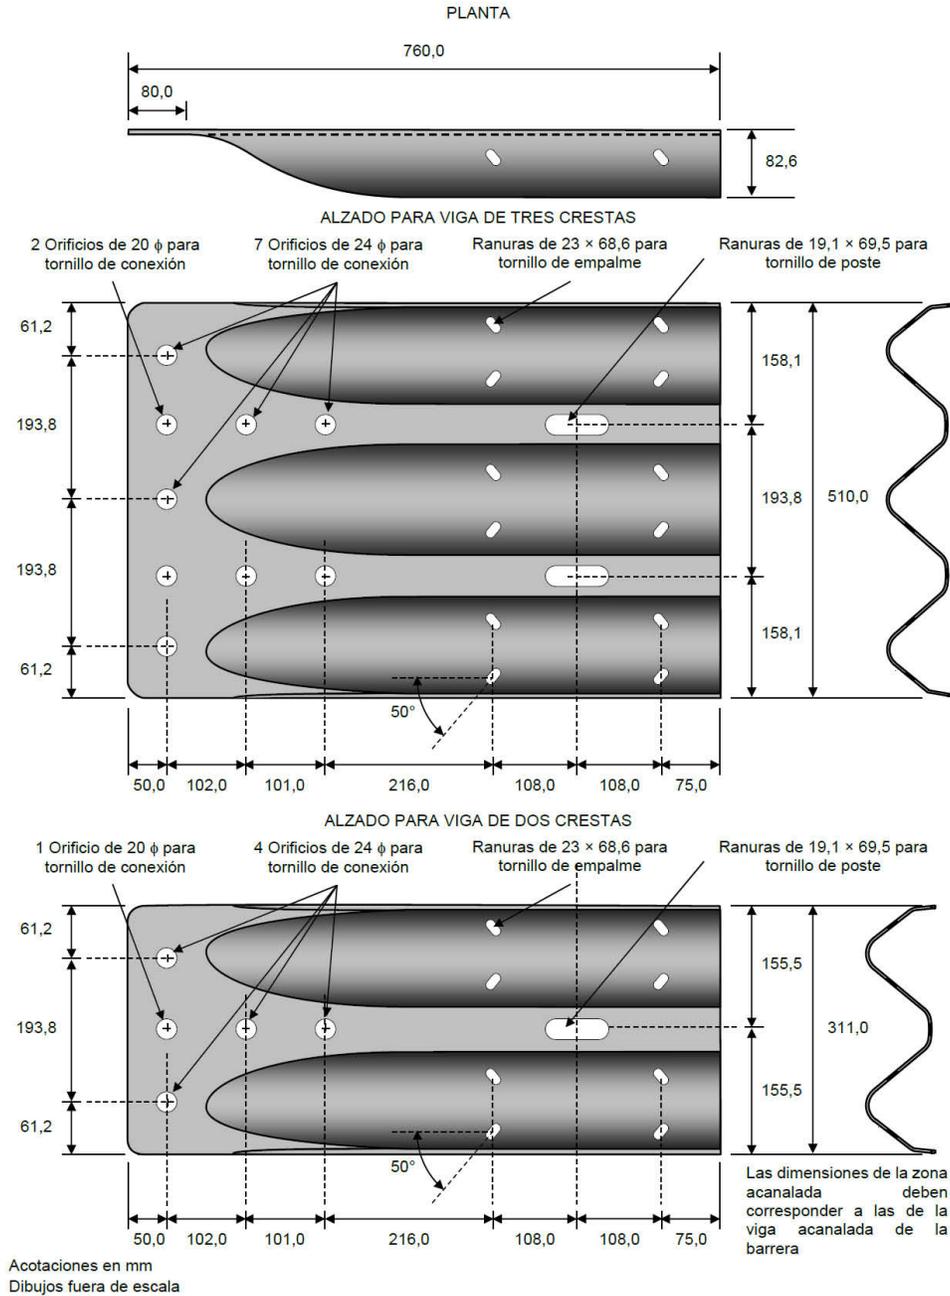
Zapatas de conexión para barreras de vigas acanaladas de acero
